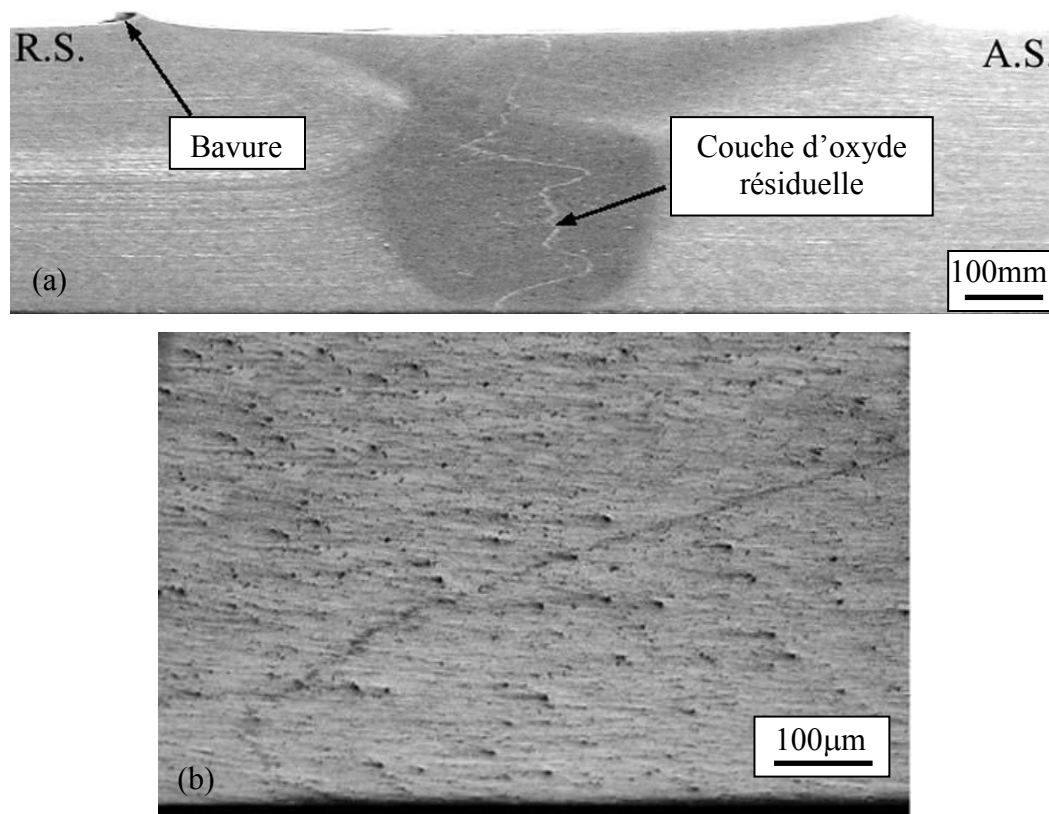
Coupe transversale dans un joint SFM en AA5083 de 8 mm d'épaisseur qui montre les bavures en surface et une ligne d'oxyde dans le joint. En (b) un agrandissement de la zone au fond du joint (Zhou, Yang et al. 2006b).
